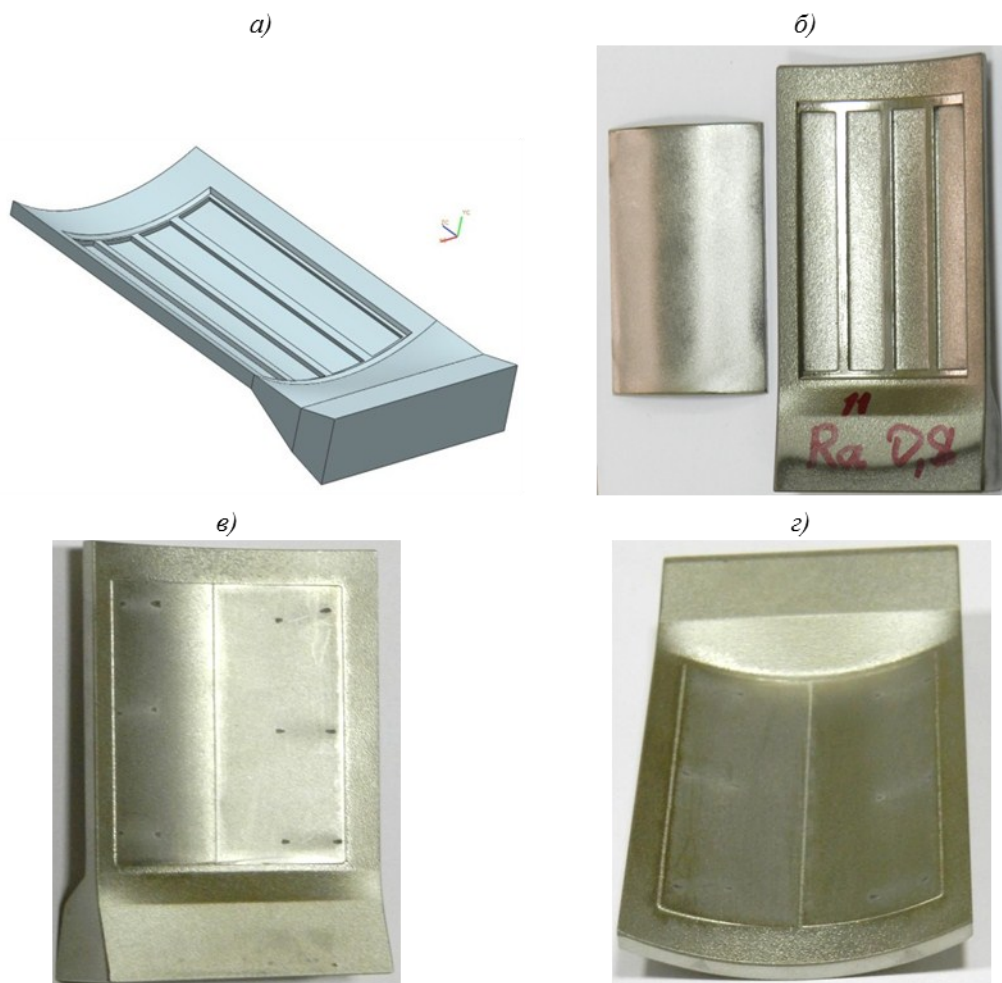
Стадии изготовления образца-имитатора двустенной лопатки методом пайки:
